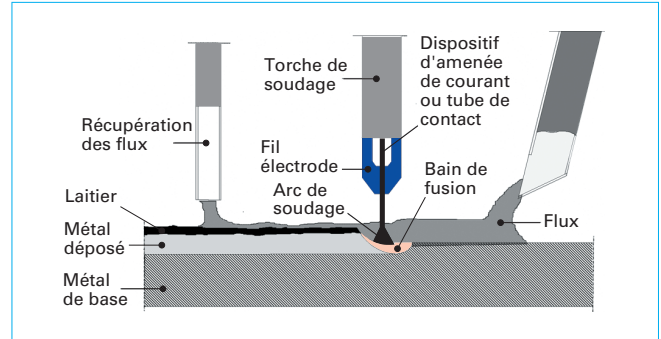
Soudage à l'arc sous flux en poudre
